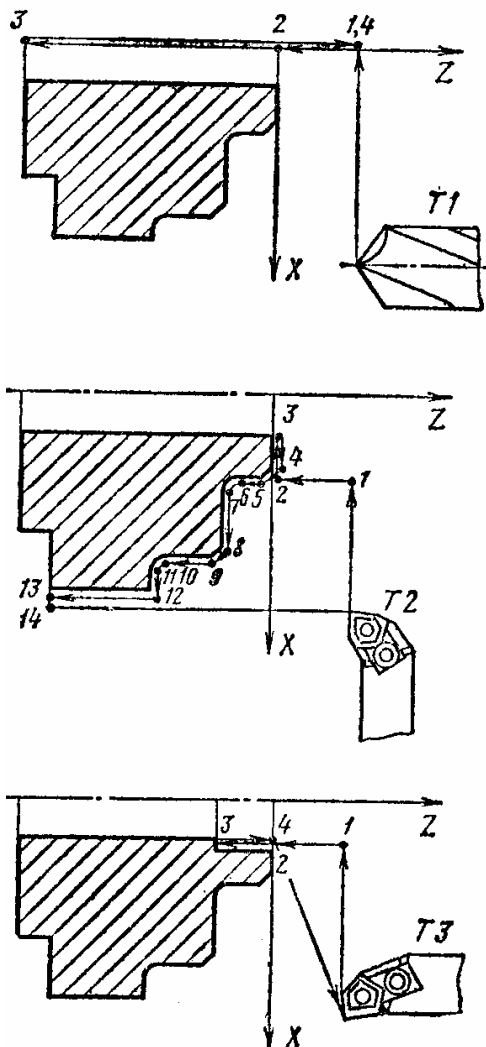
Схема обработки заготовки (к заданию 16.12.)
